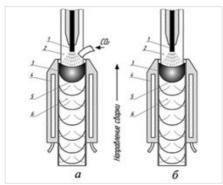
Схема электродугового процесса сварки с принудительнымформированием шва: а — в углекислом газе, б — открытой дугой. 1 — порошковая проволока, 2 — свариваемый металл, 3 — шлак, 4 — ползуны, 5 — сварочная ванна, 6 — шов.
